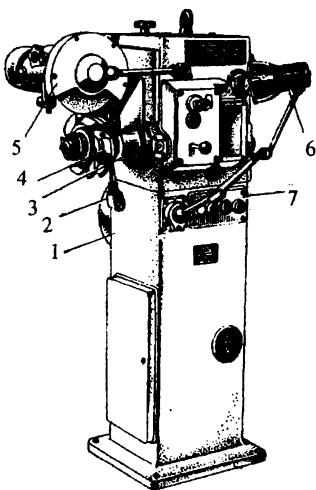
Станок ТчФА для заточки насадных затылованных фрез
